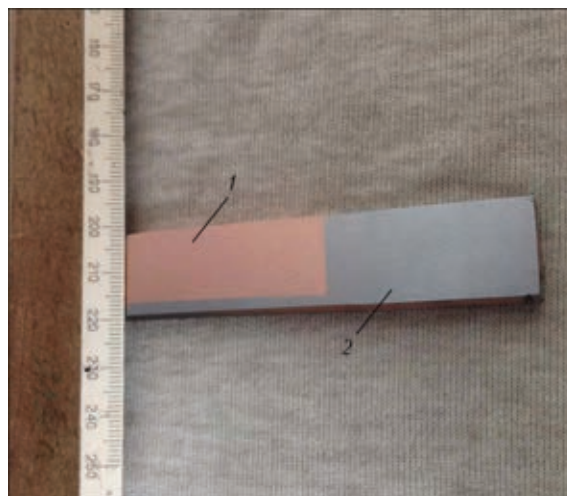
Макрошлиф сталемедного биметаллического соединения: 1 — медь; 2 — сталь
